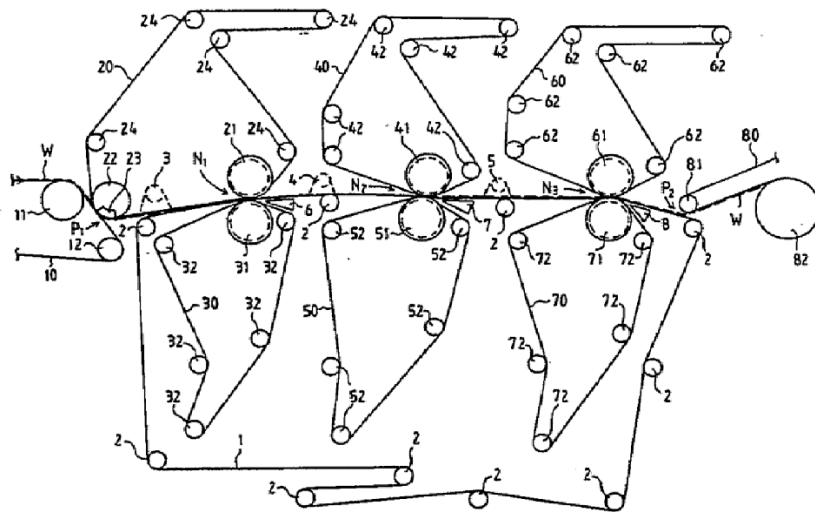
Пресова частина папероробної машини з трьома зонами пресування
